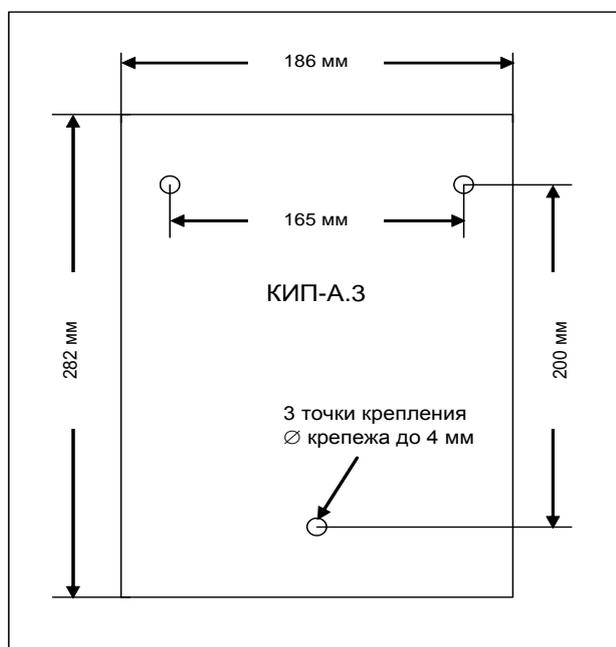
, Габаритные размеры и расположение блоков КИП-А
